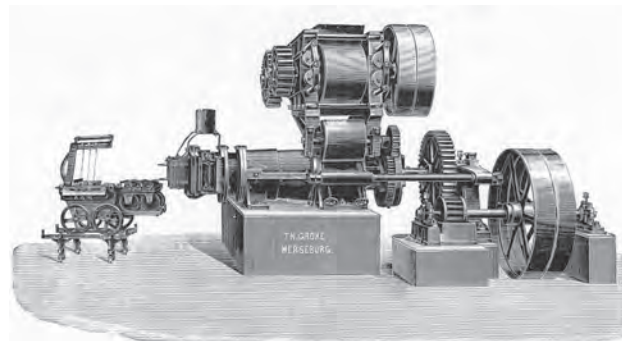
Ziegelmaschine mit aufmontiertem Walzwerk
